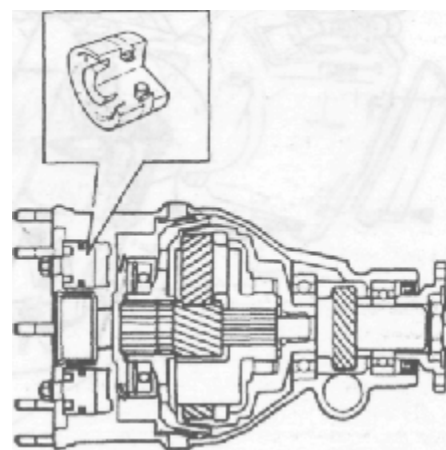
Поперечный разрез узла повышающей передачи-коробка передач М46 с типами J или P повышающей передачи
